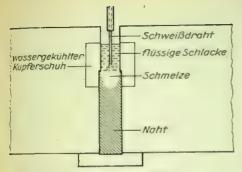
Elektro-Schlacke-(ES-)-Schweißen
